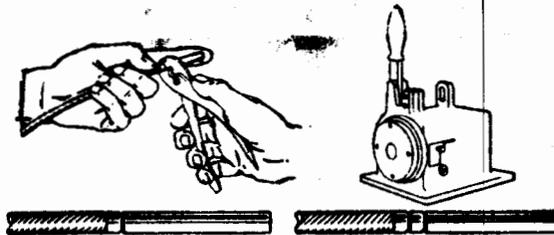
Corrugadora manual y máquina corrugadora.
